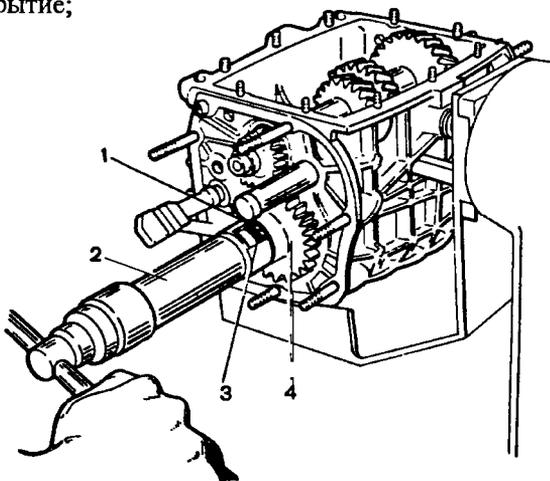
Установка на вторичном валу стопорного кольца шестерни заднего хода: 1 - запорное кольцо; 2 - оправка 41.7816.4069; 3 - пружинная шайба; 4 - шестерня заднего хода вторичного вала
